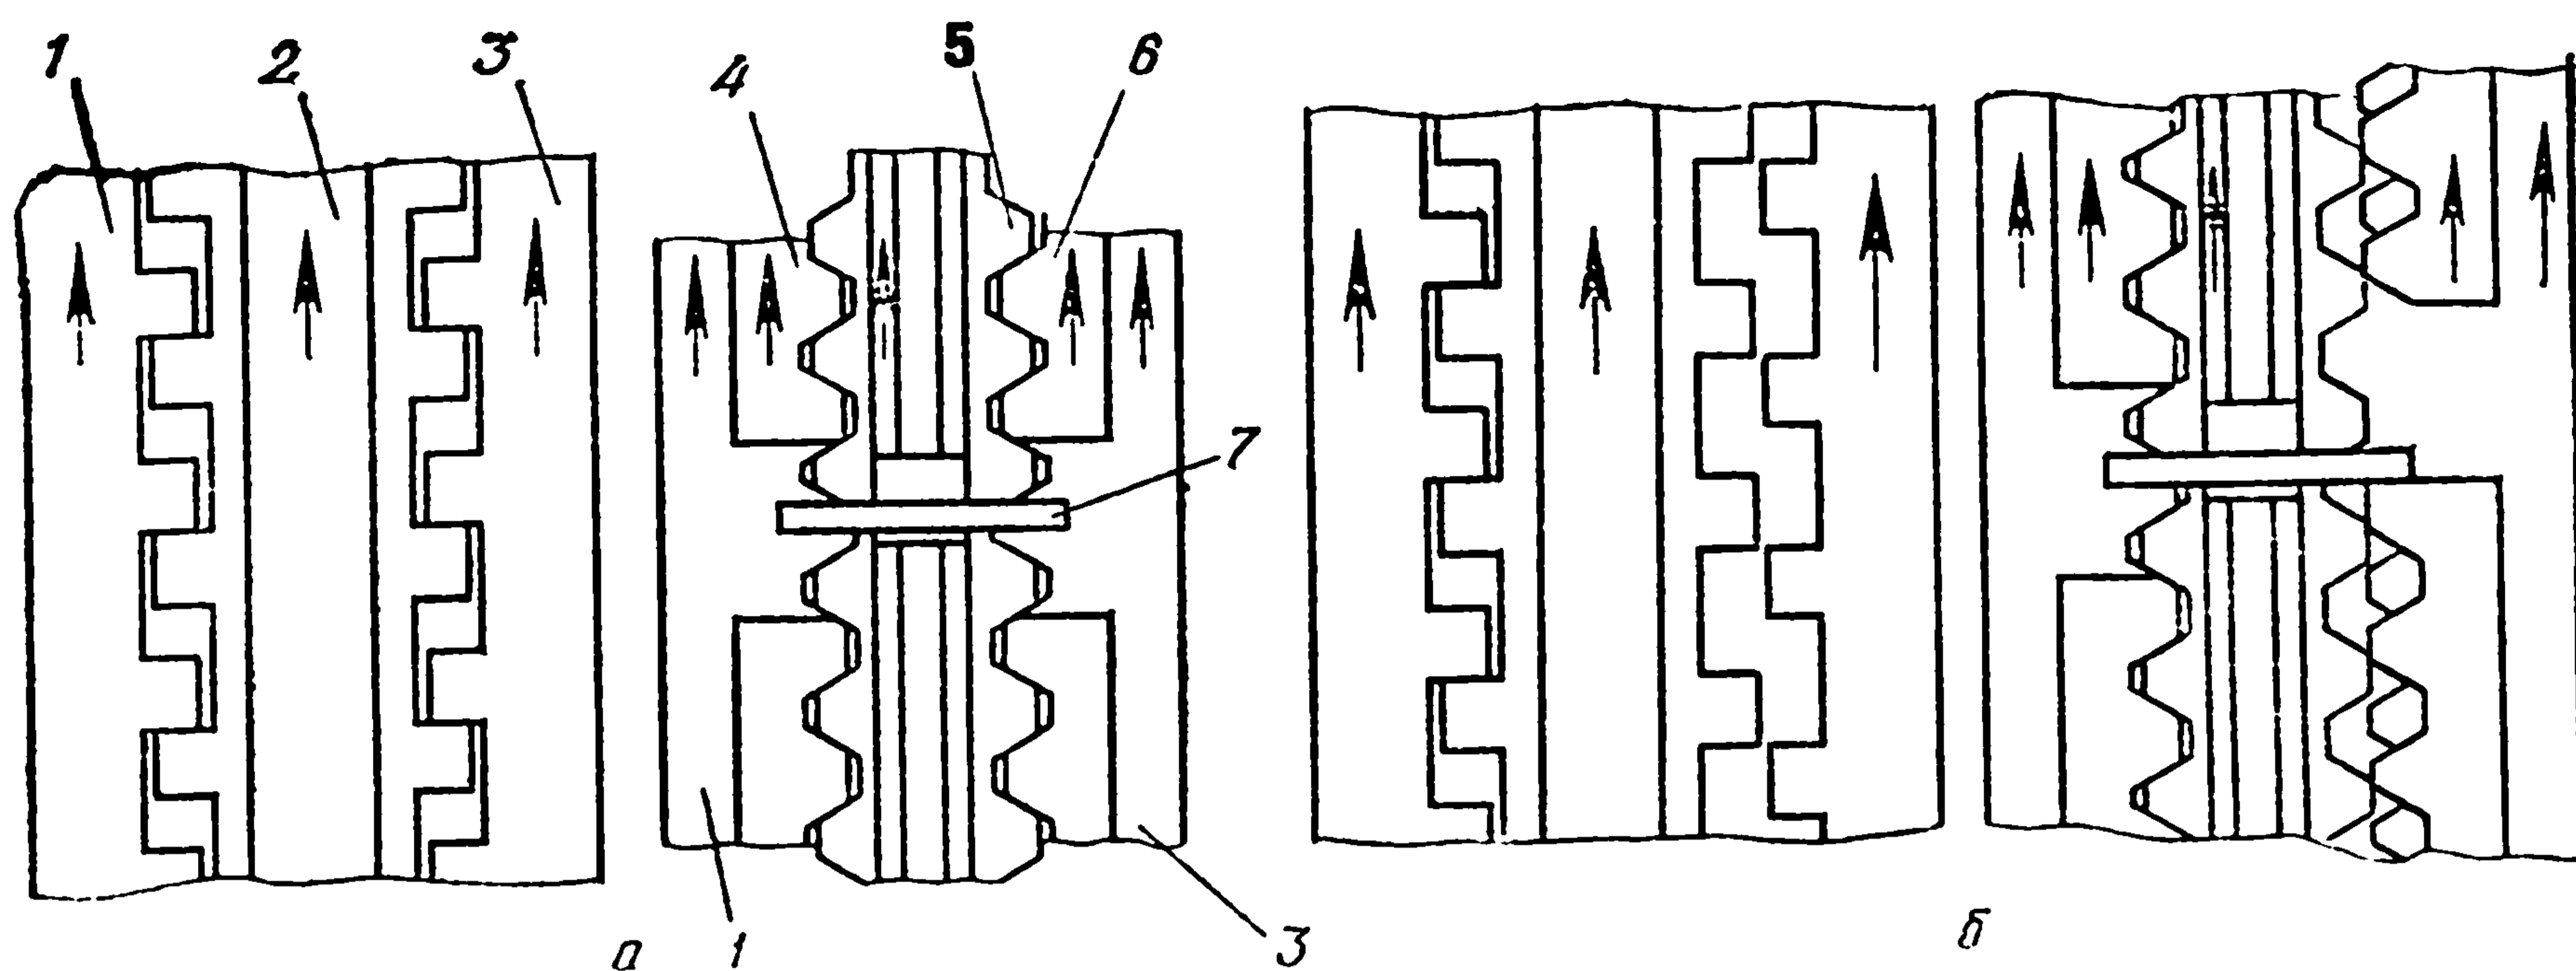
Схема работы дифференциала (развертка зацепления кулачков ведущей муфты и ее кольца с кулачками ведомых полумуфт и разрезных колец): а — прямолинейное движение; б — поворот трактора влево; 1 и 3 — ведомые полумуфты; 2 — ведущая муфта; 4 и 6 — разрезные кольца ведомых полумуфт; 5 — кольцо ведущей муфты; 7 — шпонка.
